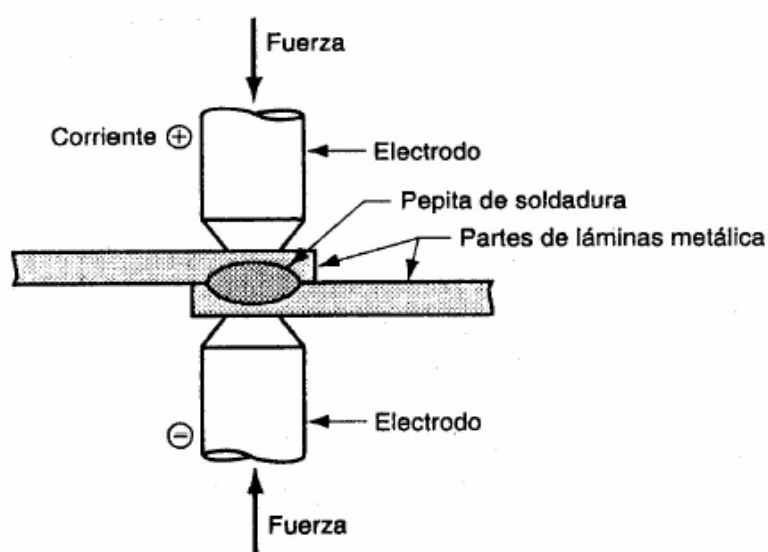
Componentes de la soldadura por resistencia
